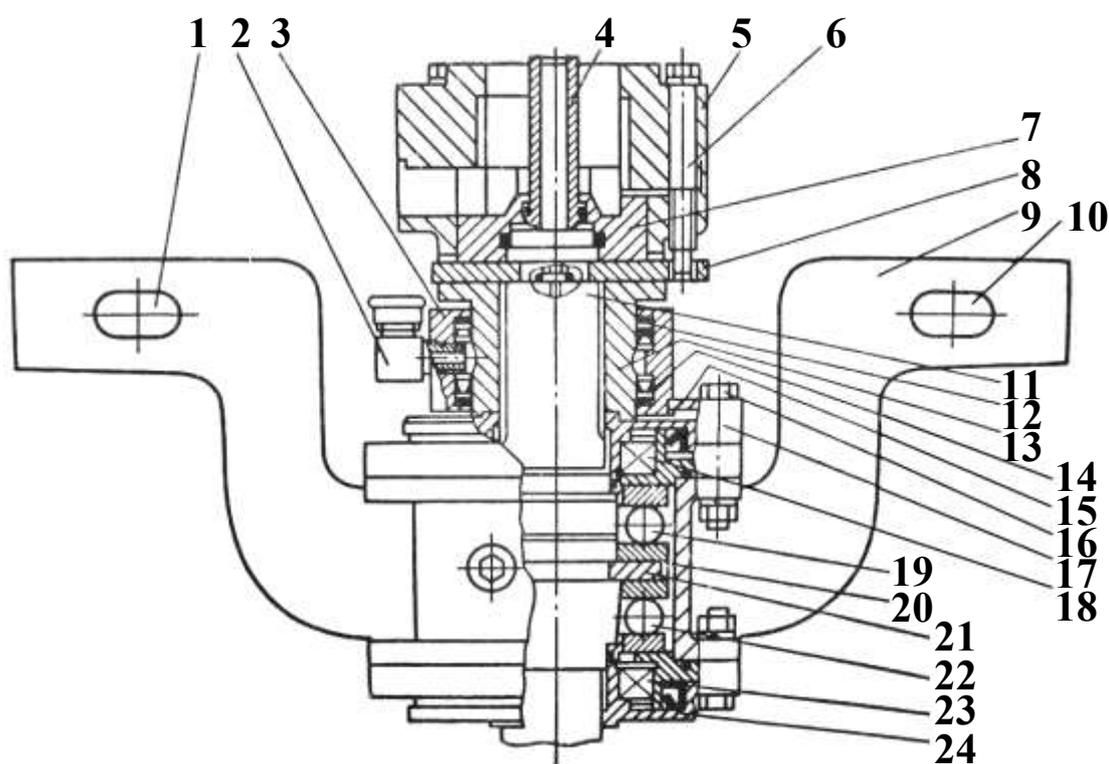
Буровой замок станков буровых установок БГА-2М и БГА-4М
